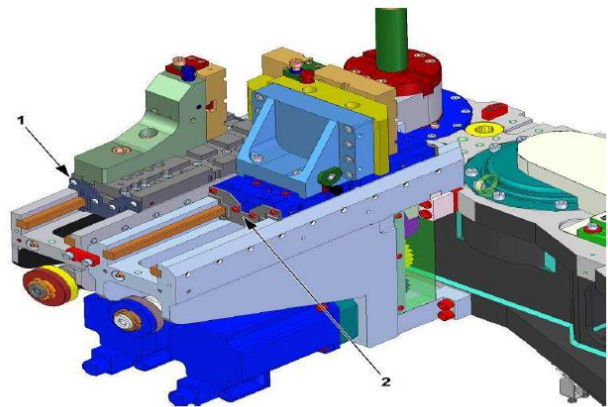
Gruppo slitta di bloccaggio tubo.
